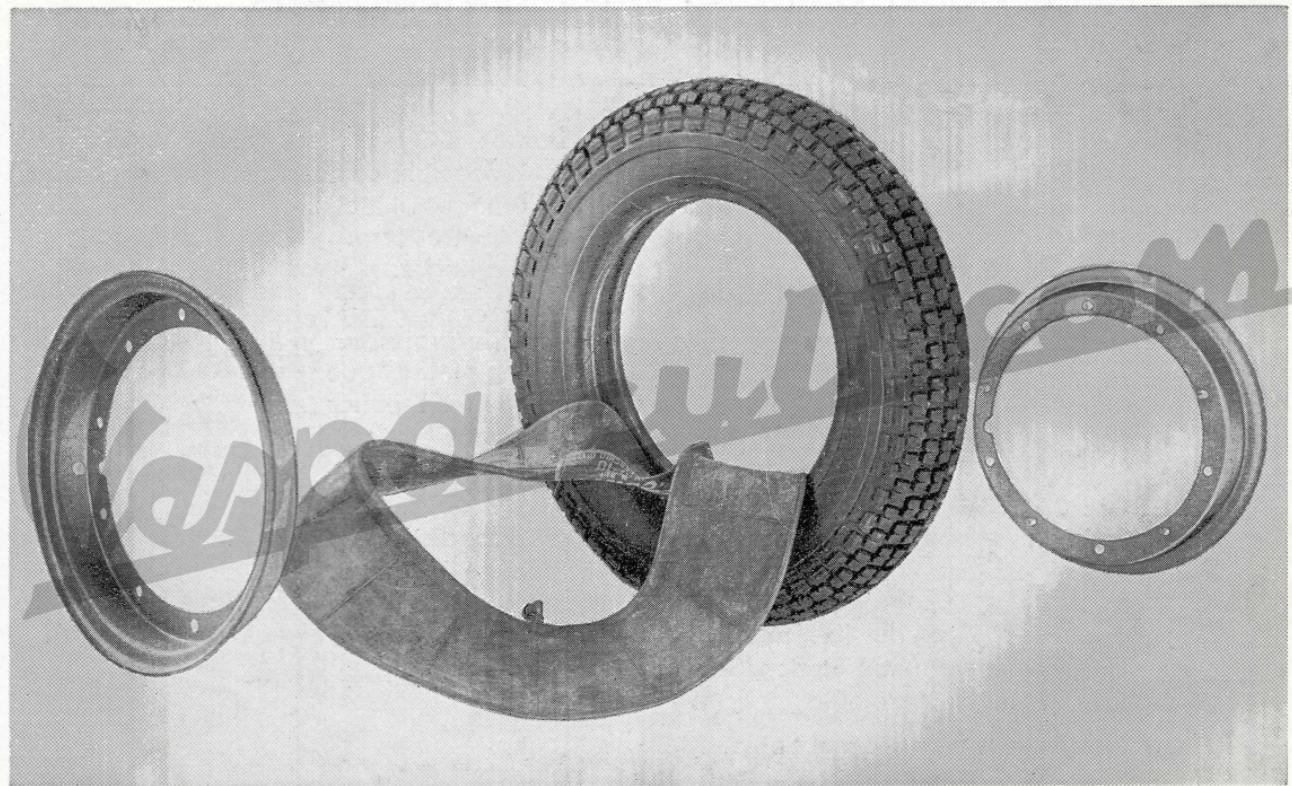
Démontage du pneu — Abb. 16 - Abmontierung des Reifens.
